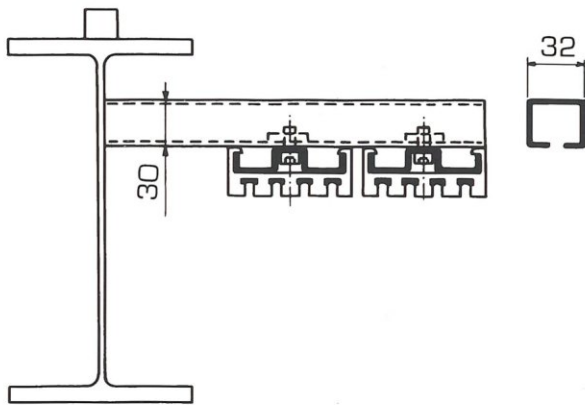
Montage sur rail de pont roulant, par supports.
